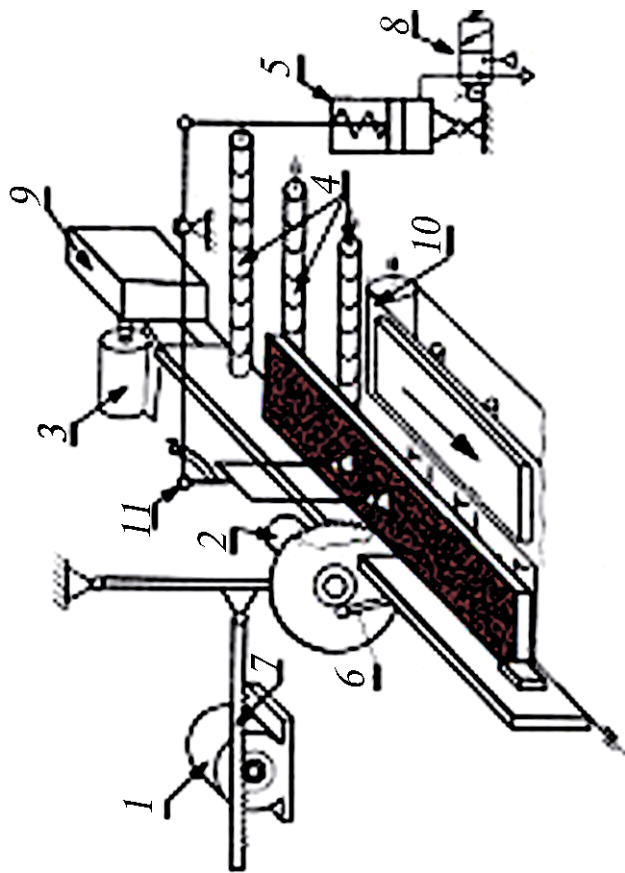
Торцовочный станок для обработки деревянных изделий
